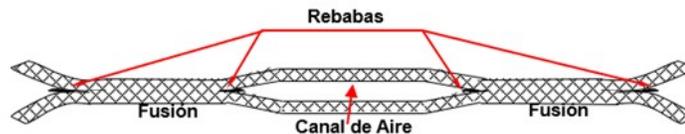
Esquema soldadura por cuña caliente.
